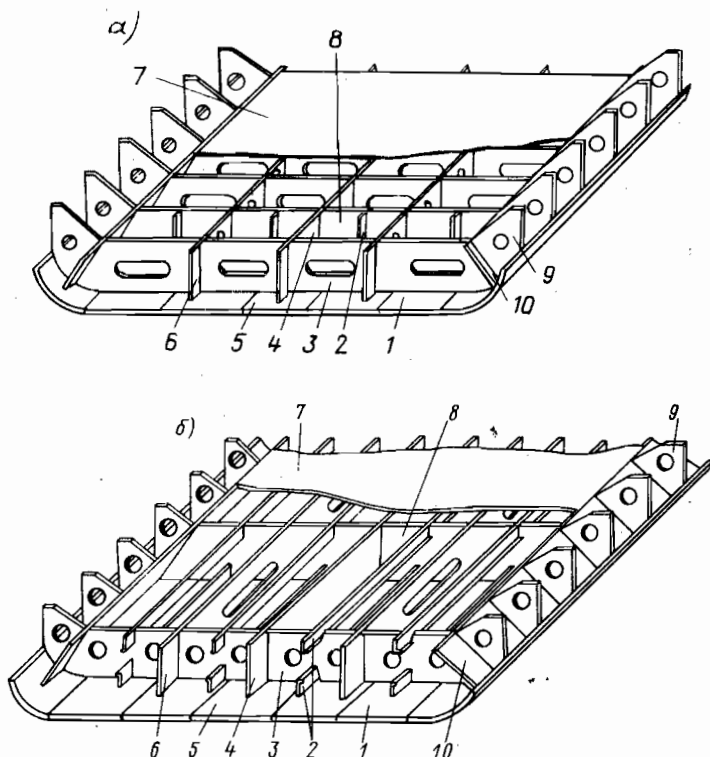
Конструкция днищевого перекрытия с двойным дном:
